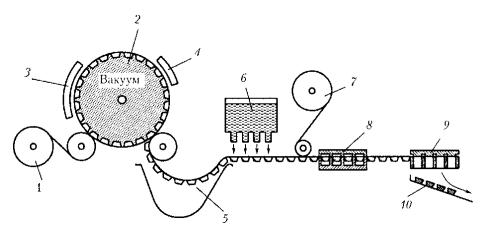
Схема линии упаковки с вакуумформовкой тары:
